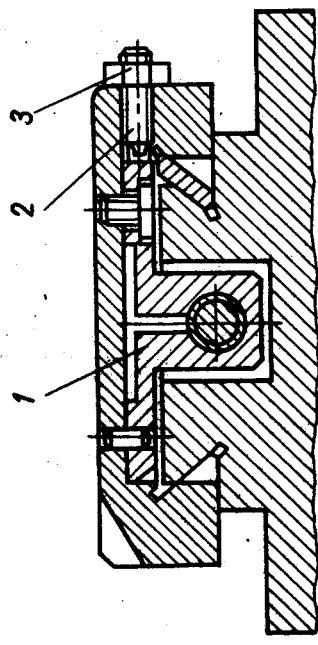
Регулировка зазора в резьбовом соединении верхней каретки суппорта
